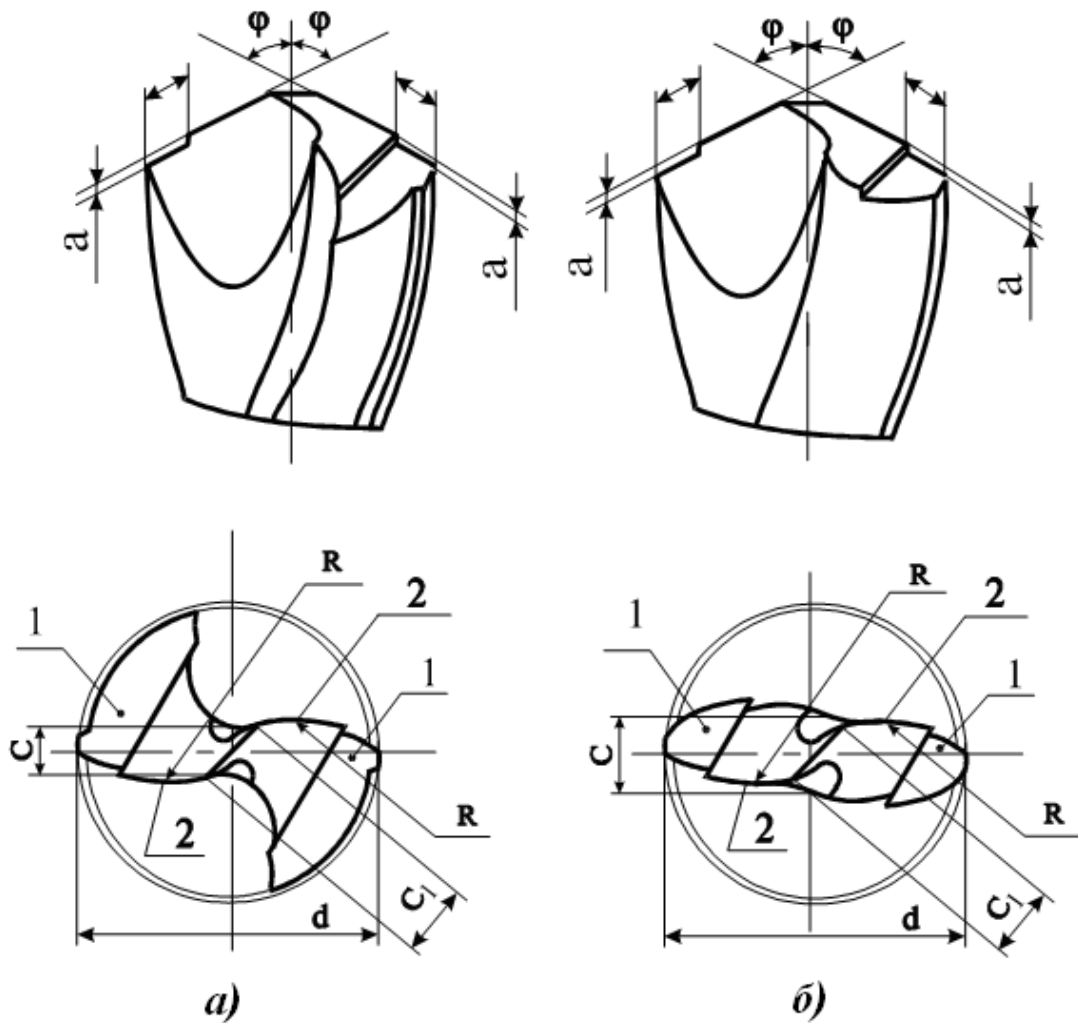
Форма заточки вершины спирального сверла с элементами дробления стружки.
